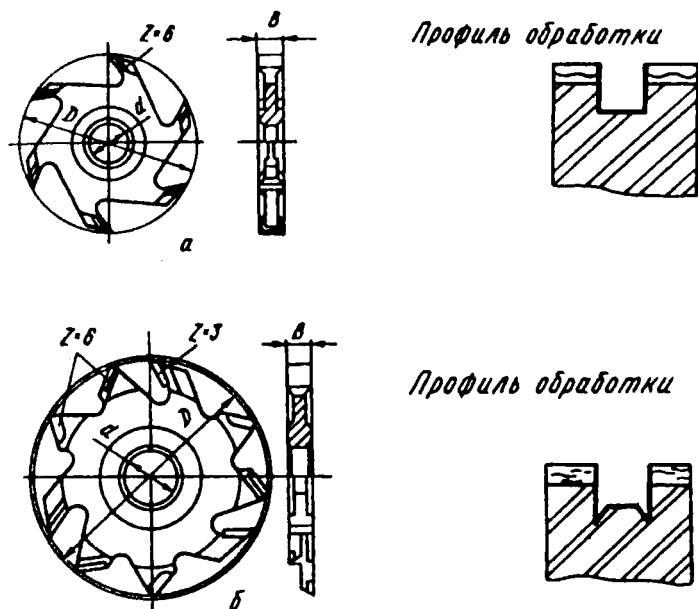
Фрезы для фрезерования прямоугольных шипов:
